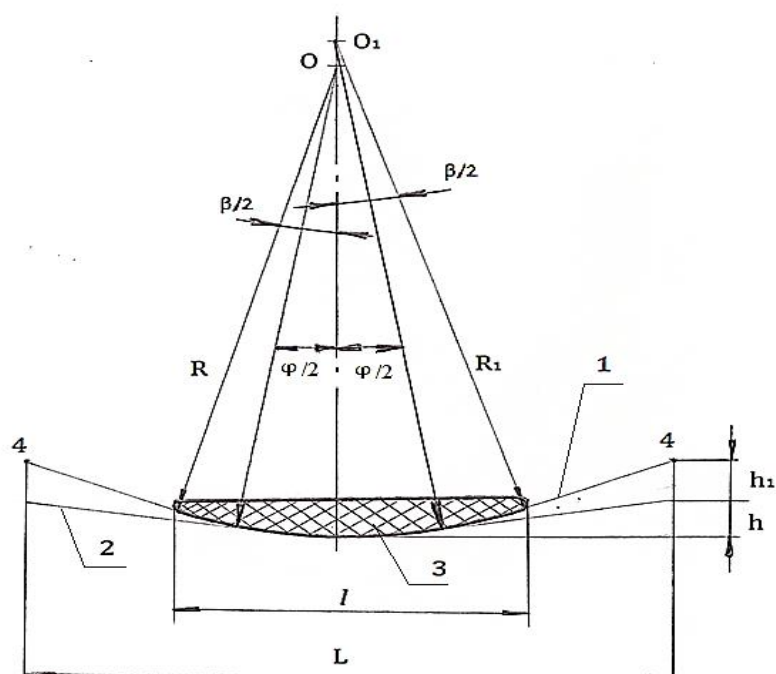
Предлагаемая форма ситалловой накладки тормоза уточной нити станка СТБ
